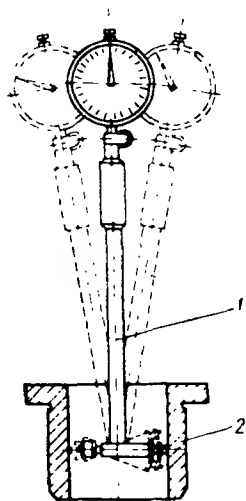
Измерение внутреннего диаметра кольца роликового подшипника индикаторным нутромером:
